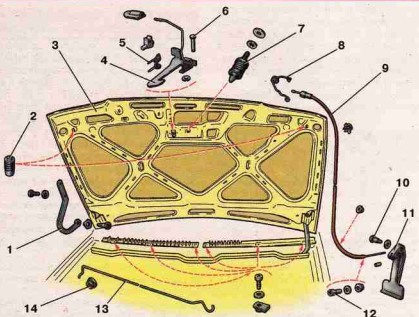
Детали капота и замка: 1 – петля капота; 2 – буфера; 3 – капот; 4 – крючок; 5 – пружина крючка; 6 – ось крючка; 7 – штырь; 8 – пружина замка; 9 – оболочка с тягой замка; 10 – ось рукоятки; 11 – рукоятка замка; 12 – втулка оболочки тяги; 13 – оболочка с тягой замка; 14 – втулка упора капота
